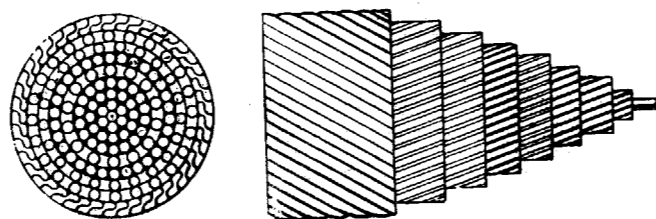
Cable enclavado anti-giratorio de auto-apriete.
